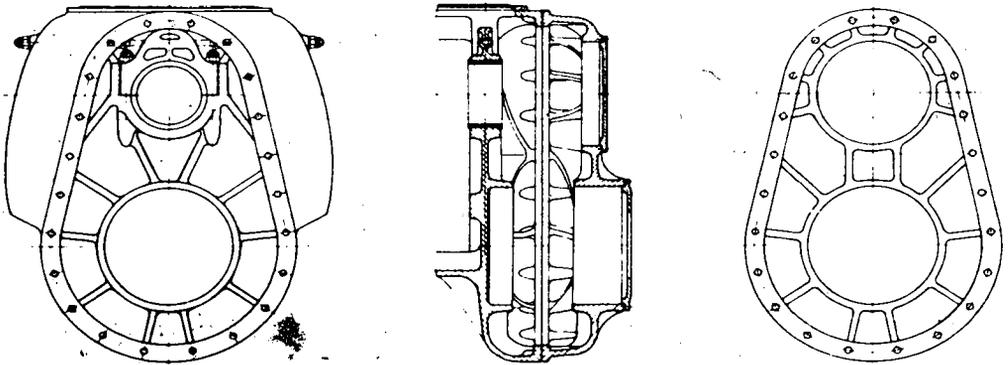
Beispiel für die Ausführung des Getriebehäuses bei einem Reihenmotor
